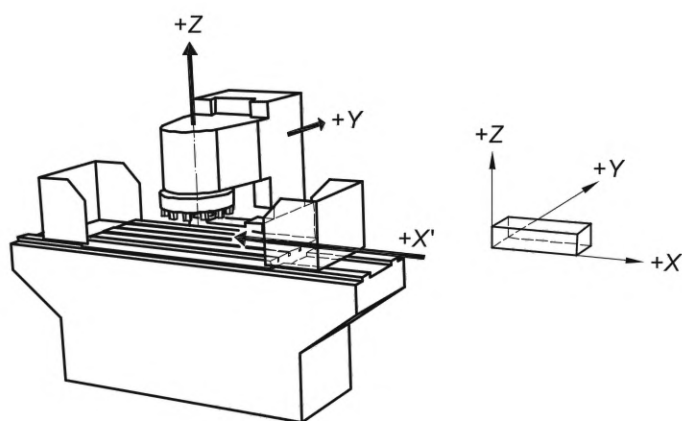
Продольно-шлифовальный станок с вертикальным шлифовальным кругом
